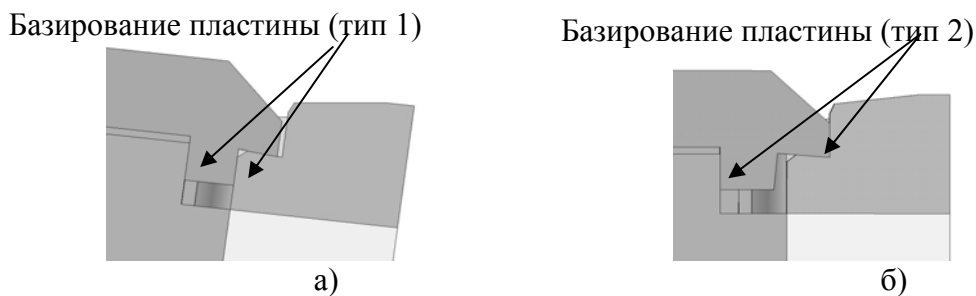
Варианты базирования режущей пластины сборного резца:
